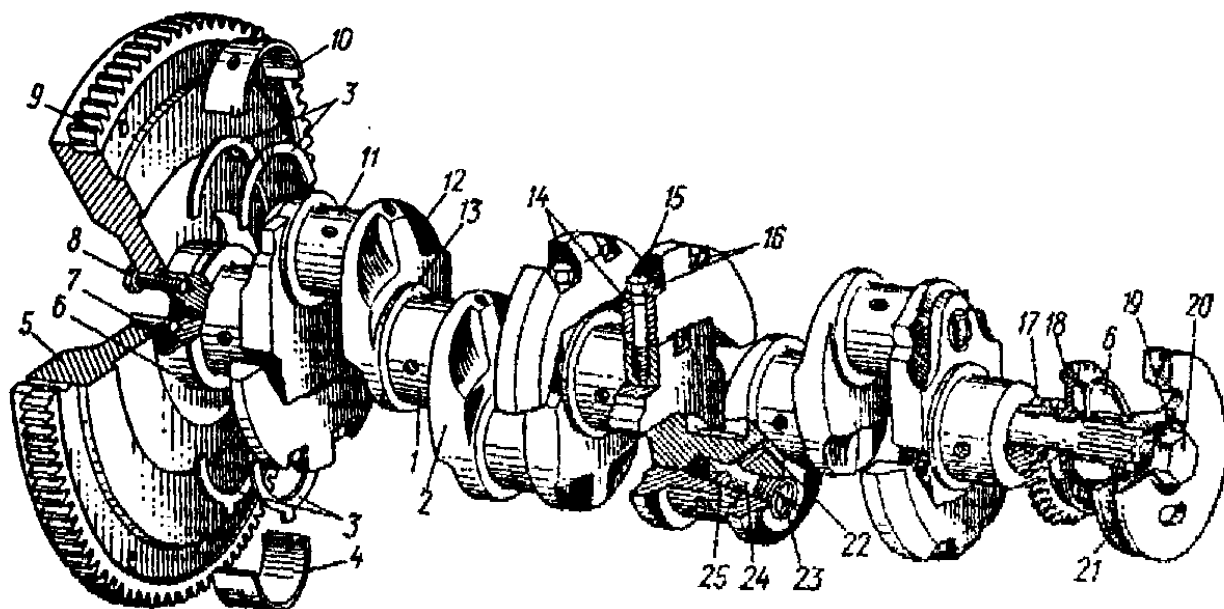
Коленчатый вал в сборе двигателя ММЗ Д-243 трактора МТЗ-80
